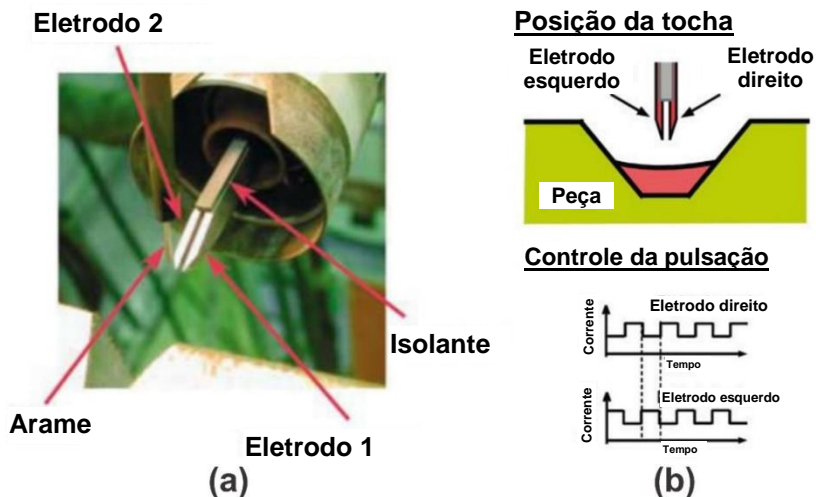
Tocha de soldagem TIG duplo eletrodo utilizada por Kobayashi et al. [20]
